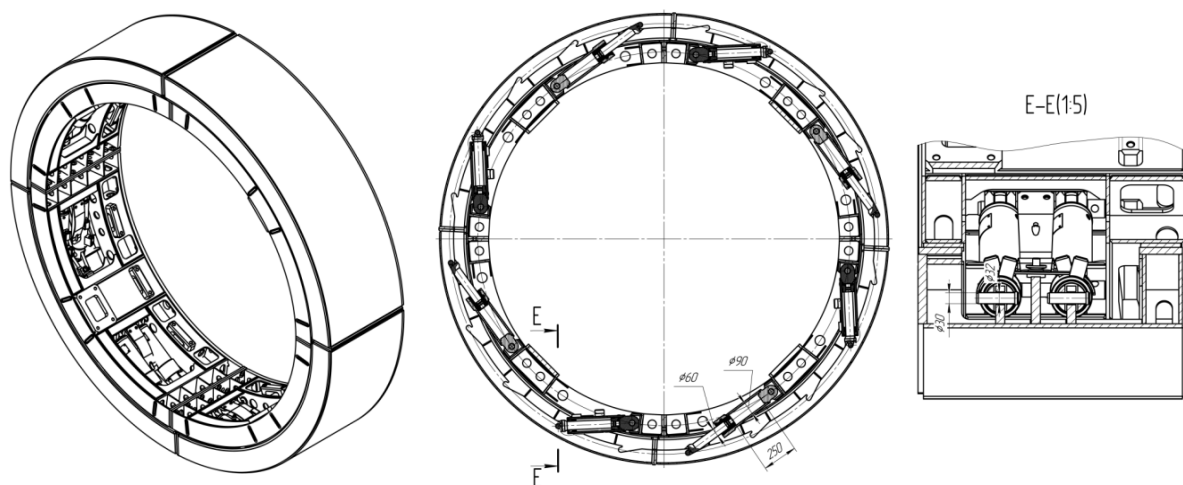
Виды со сборочного чертежа узла сопряжения секций опытного образца геохода
